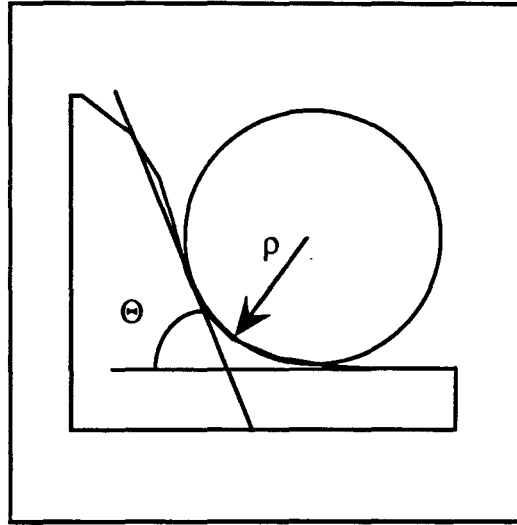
Définition des paramètres ρ (rayon de raccordement) et Θ (angle de raccordement) en pied de cordon de soudure
